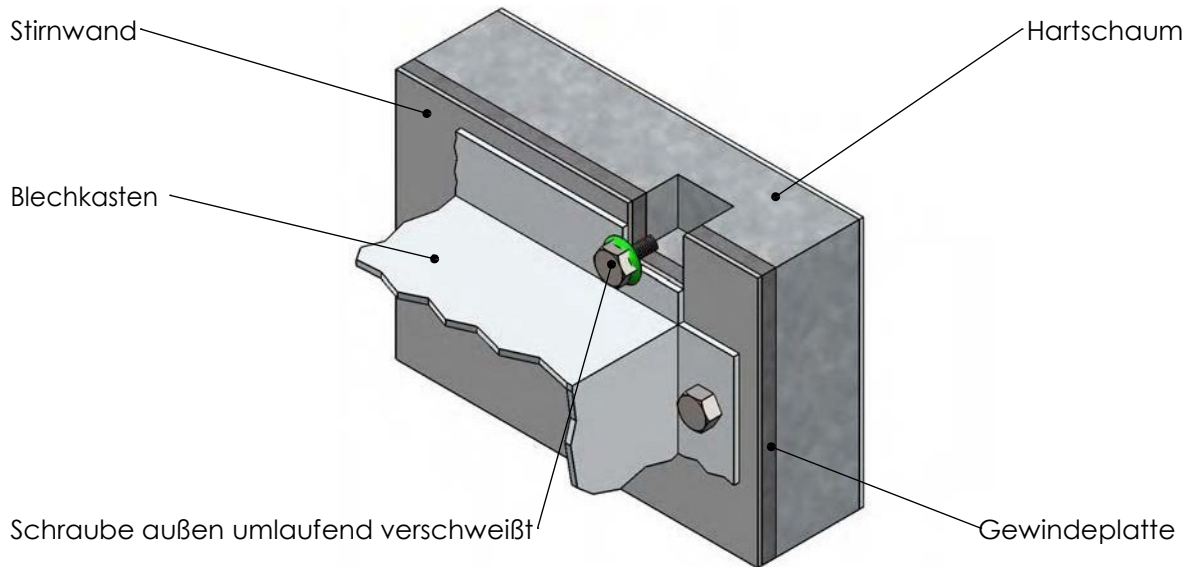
Sicherung mit außen verschweißten Schrauben
